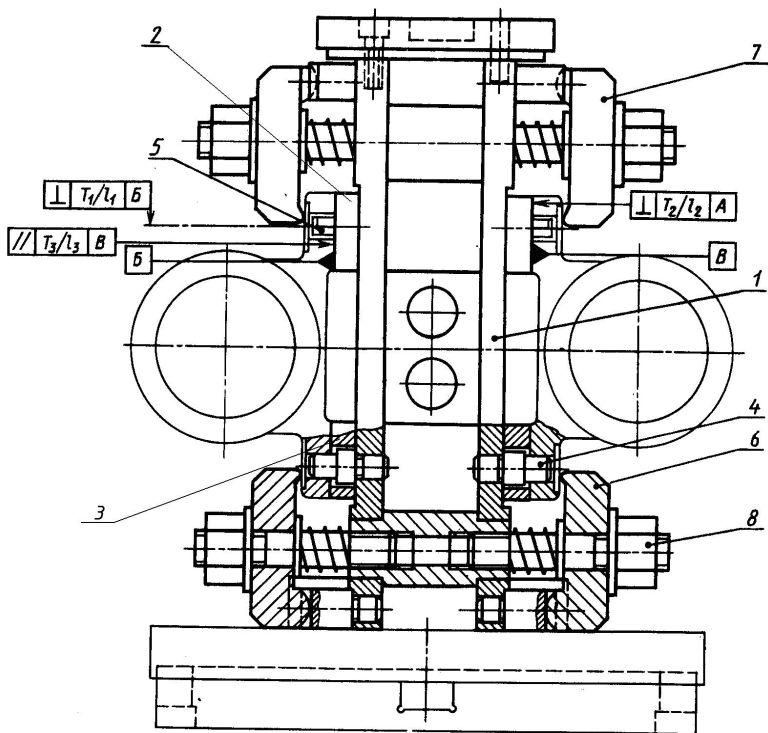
Двухместное приспособление для установки корпуса подшипника:
